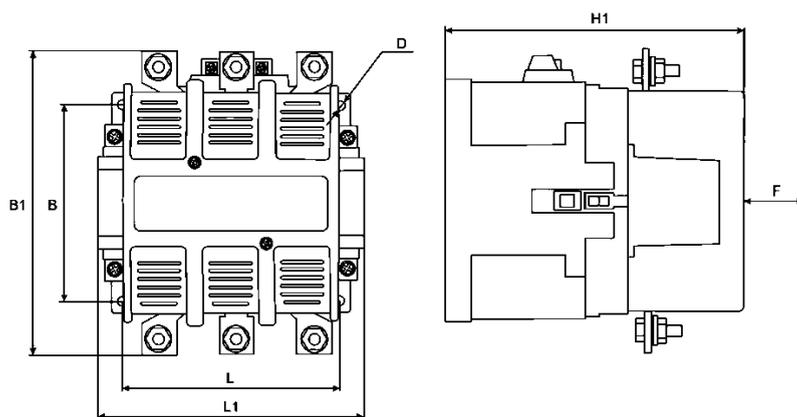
Пускатель неперевсивный ПМ12 315-1250А, IP00
